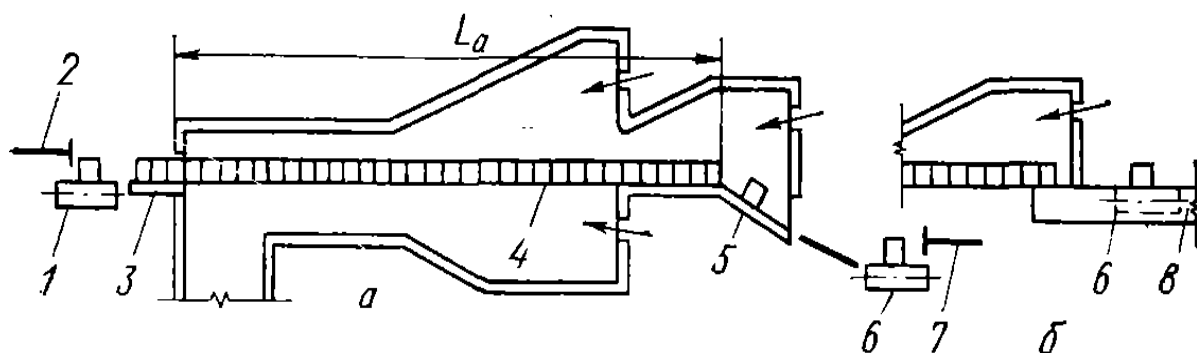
Схема транспортирования заготовок с торцовой загрузкой и торцовой выдачей
